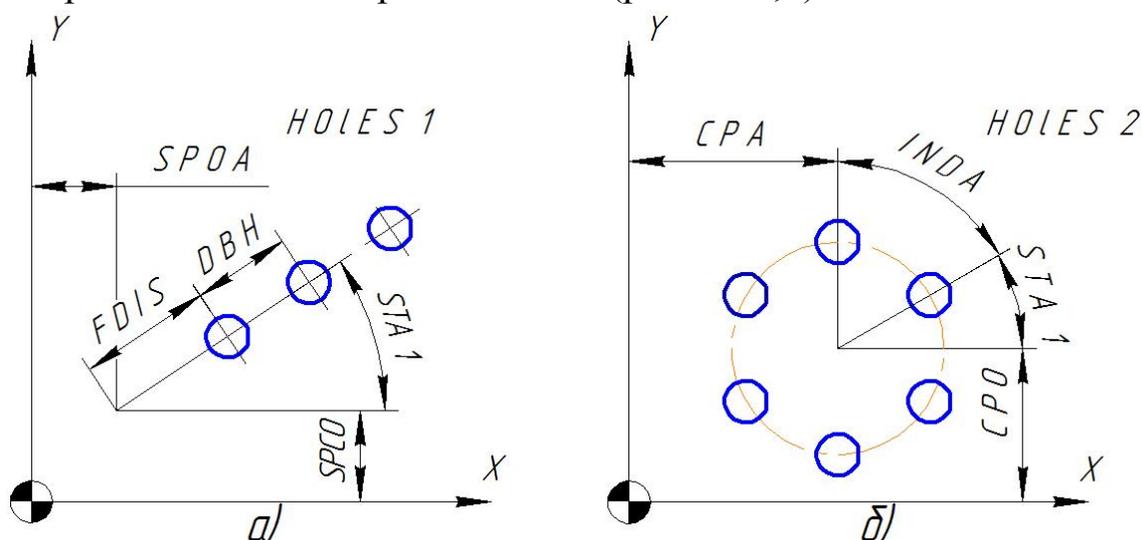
Параметры циклов: а – HOLES1, б - HOLES2
